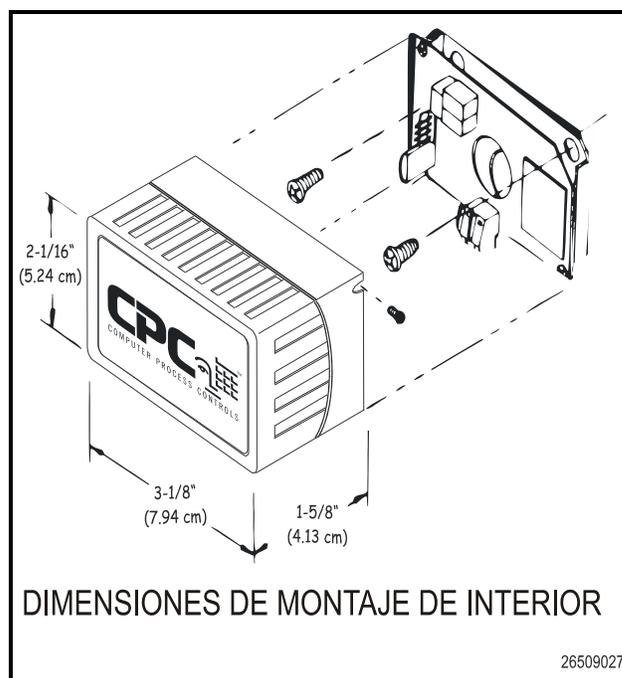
Dimensiones de Montaje del RH de Interior
